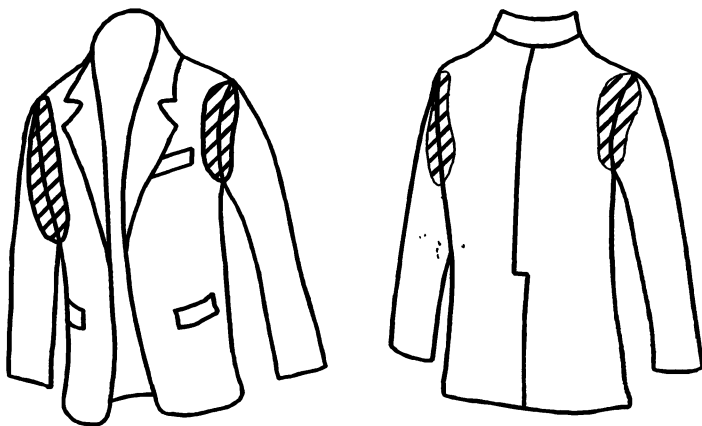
Схема расположения обрабатываемых участков пройм рукавов
